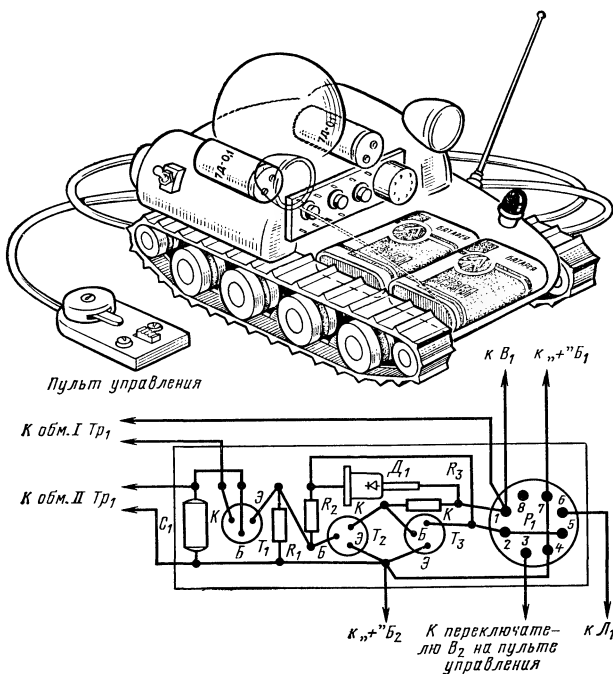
Конструкция модели и схема соединения деталей на монтажной плате.
